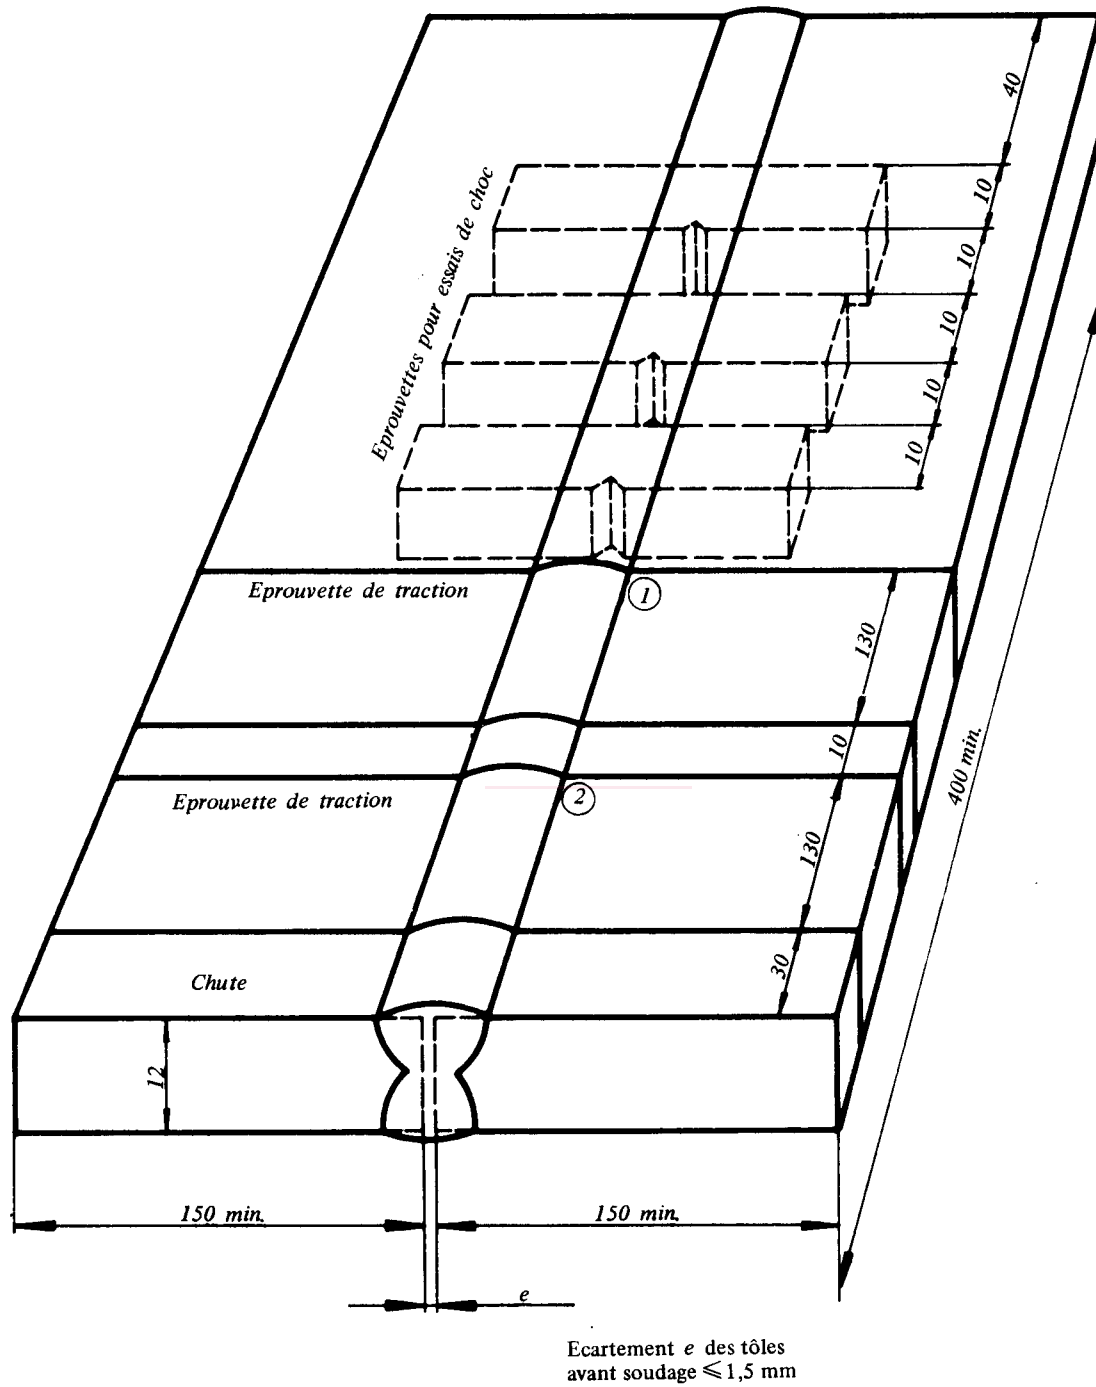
Emplacement des éprouvettes dans l'assemblage soudé
